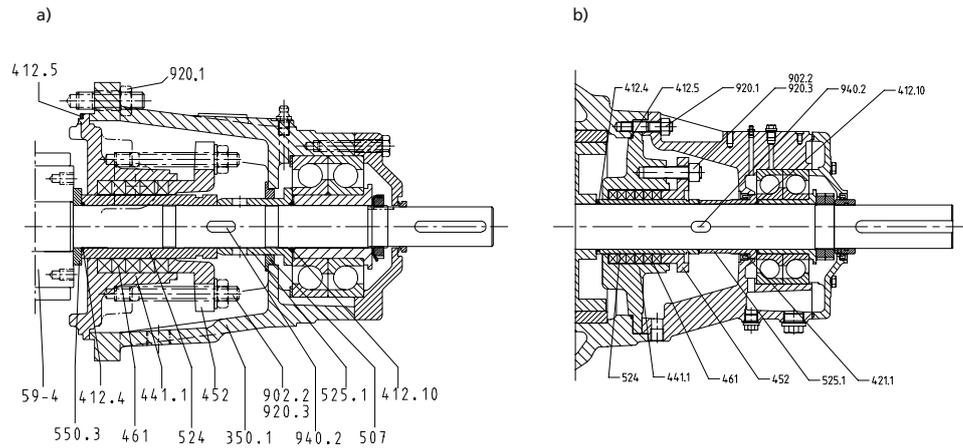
Desmontaje de la empaquetadura del prensaestopas: a) Tamaño 32-200 y b) Tamaño 250
